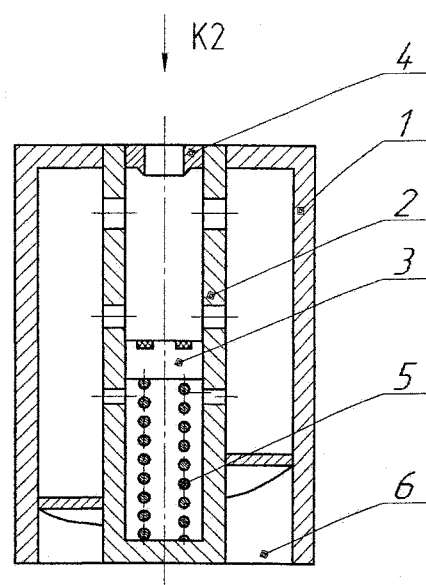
Однокомпонентная многорежимная форсунка: 1 – внешний корпус; 2 – внутренний корпус; 3 – поршень; 4 – седло; 5 – пружина; 6 – сопло
